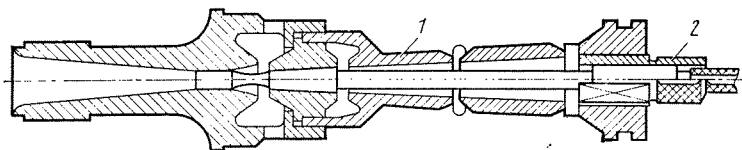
Проверка соосности сопел инжектора с помощью калибров:
